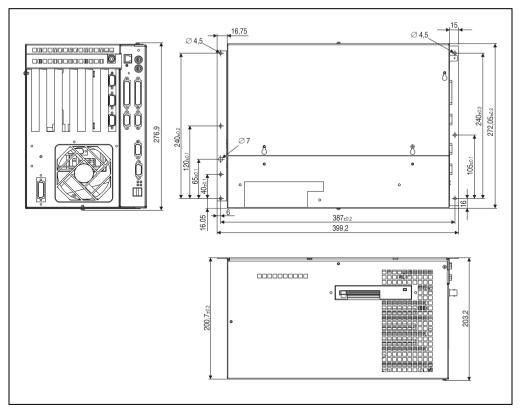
Dimensions IPC5600 / IPC5600C (6 emplacements)
